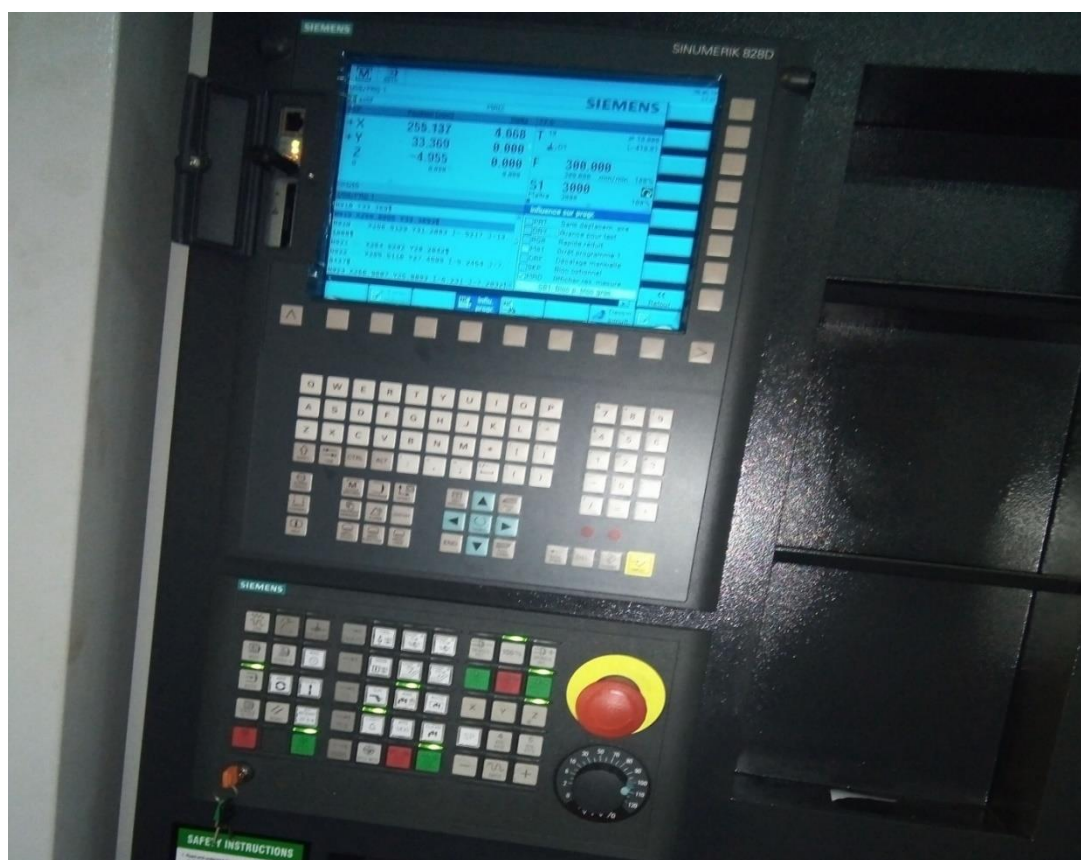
Pupitre opérateur de la fraiseuse Mill-Metric LEADWELL V-40iL.
